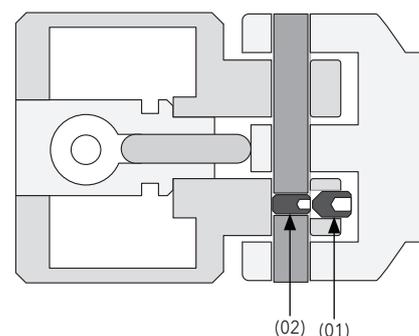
support de bras articulé en coupe - vis pointeau placées l'une derrière l'autre
